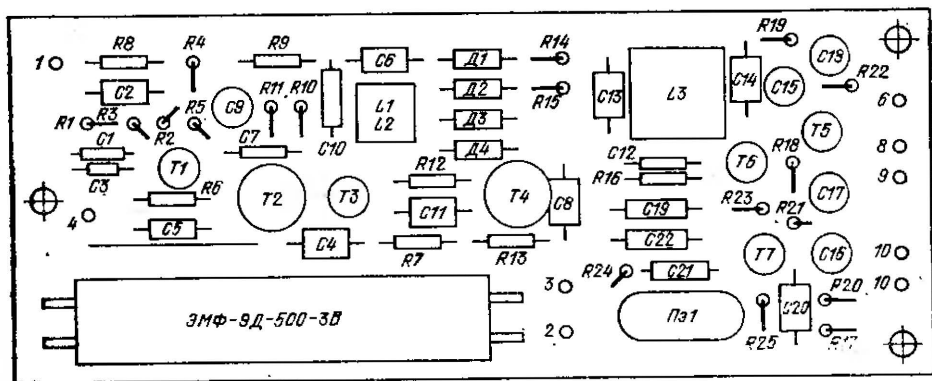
Монтажная схема платы усилителя ПЧ (вид сверху)
